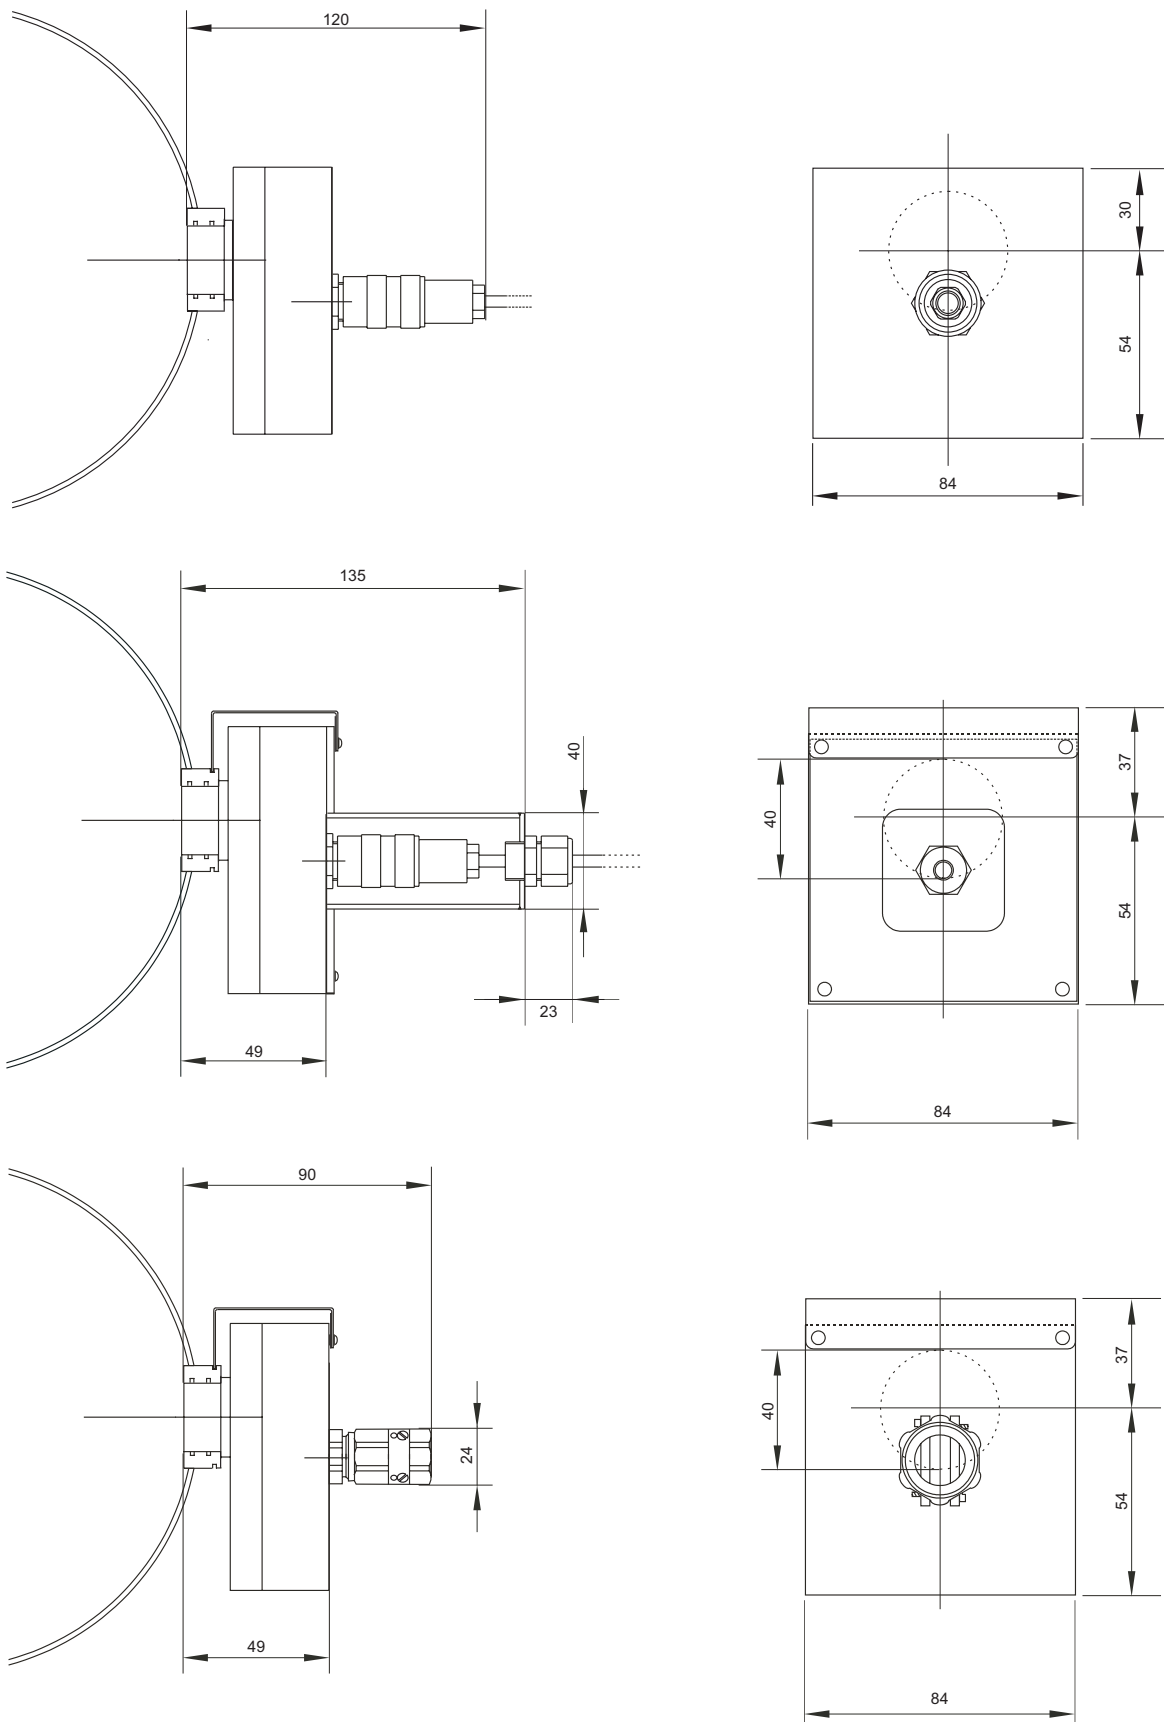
dimensions de montage avec utilisation d'un support soudable FM 1/8
